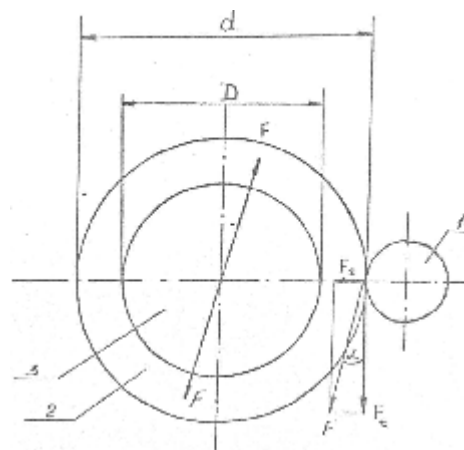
Схема сил, що діють на голковий циліндр круглов'язальної машини типу КО: 1- циліндрична зубчаста шестерня; 2 – циліндричне зубчасте колесо; 3 – опорна частина голкового колеса
